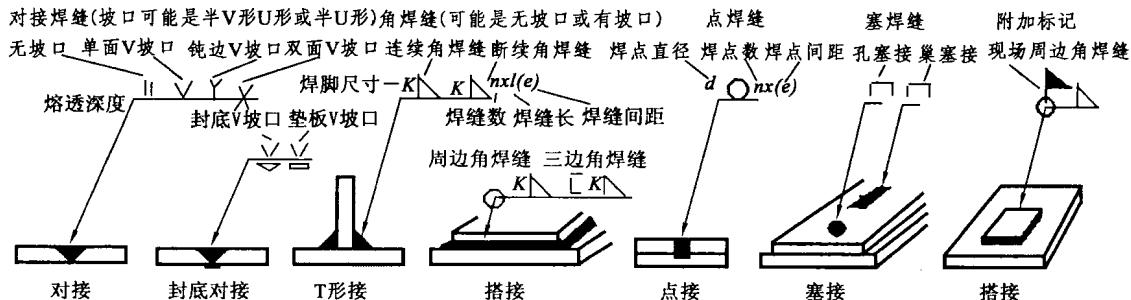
焊接结构图纸上焊接接头接头形式的代号
